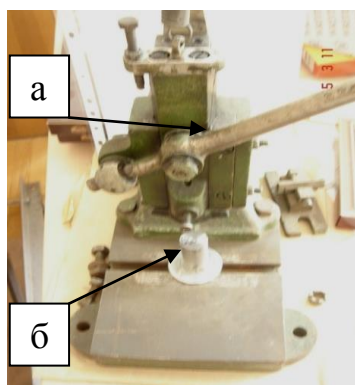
Станок для холодного прессования: а - рычаг прессования; б - пресс-форма
